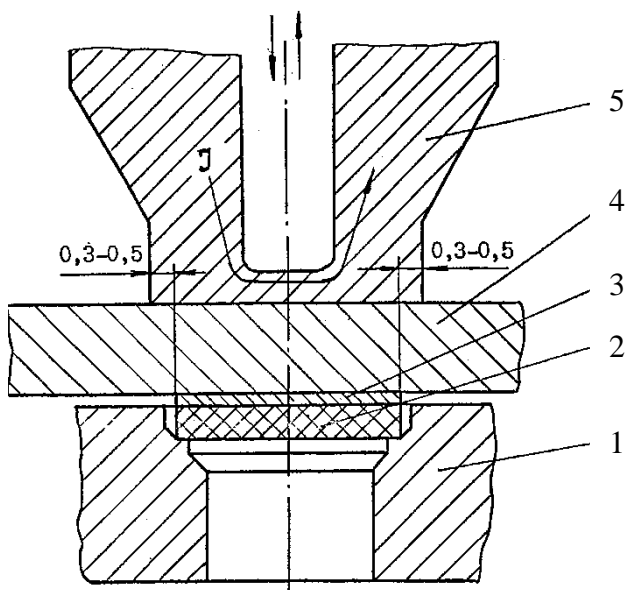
Схема пайки одного кристалла: 1 – вакуумная присоска; 2 – кристалл; 3 – припой; 4 – выводная рамка; 5 – U-образный электрод
